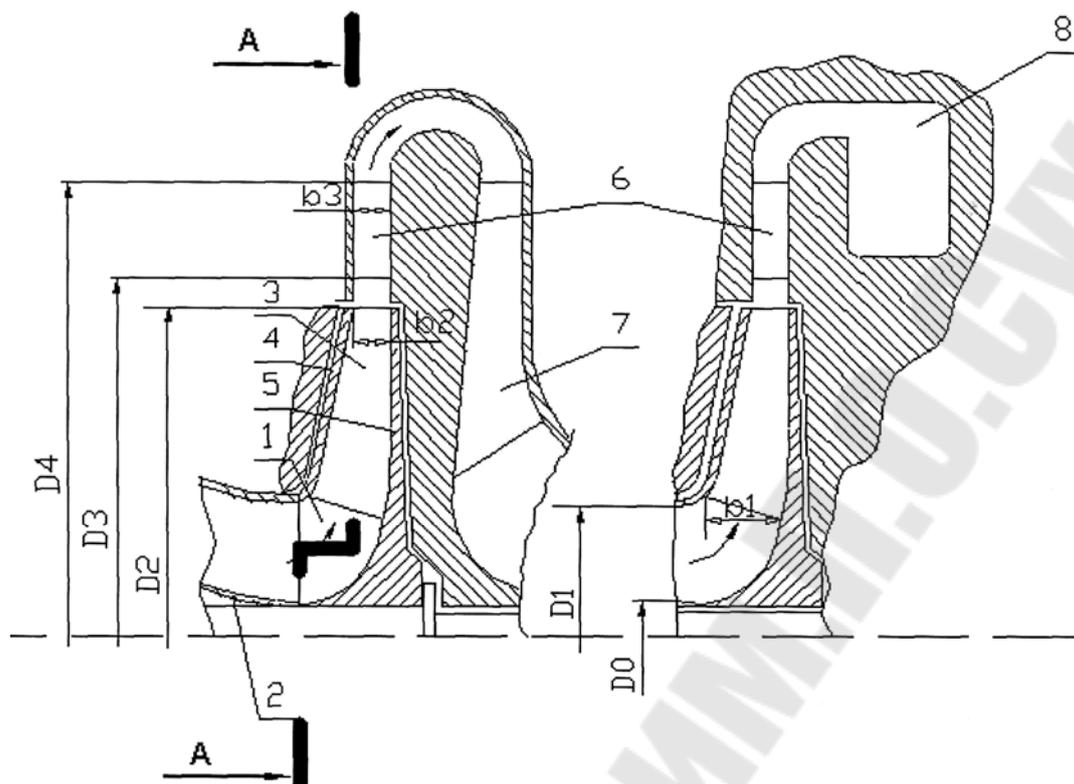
Продольный разрез ступени центробежного компрессора:
